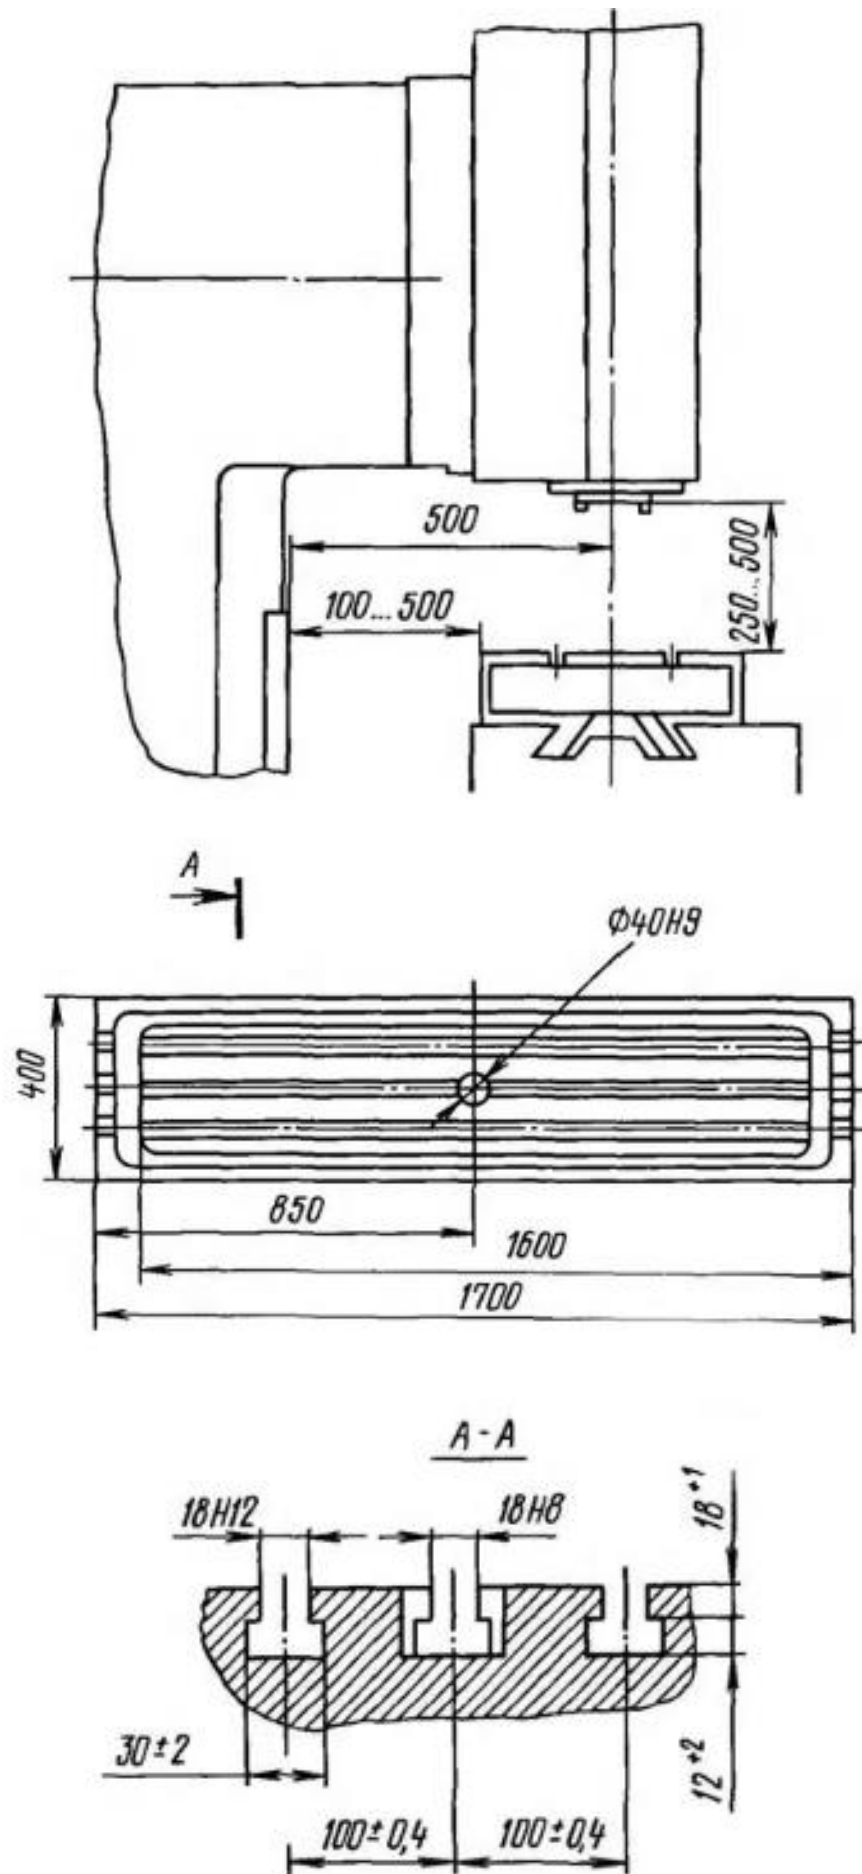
Габаритні розміри робочого простору верстата [2]
